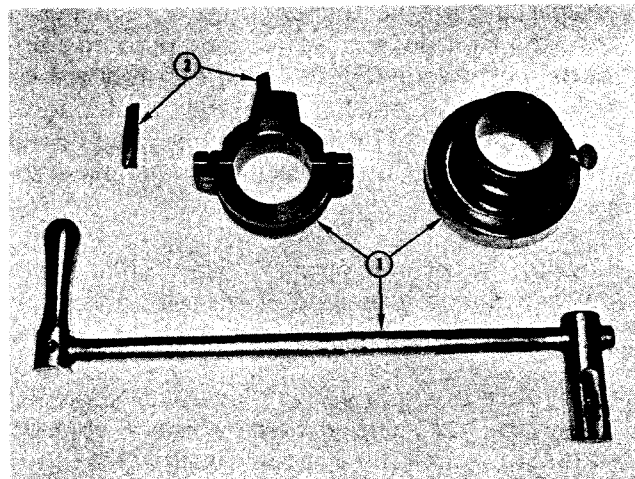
, (N101118). Cortadora del ajuste longitudinal 3375053.
